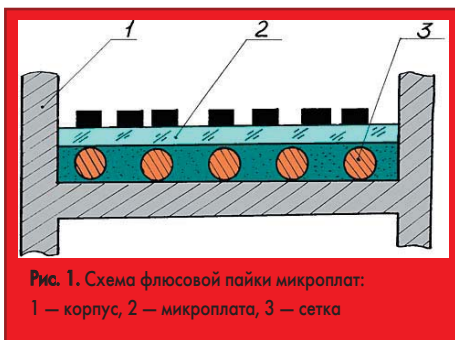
Схема флюсовой пайки микроплат: 1 — корпус, 2 — микроплата, 3 — сетка
